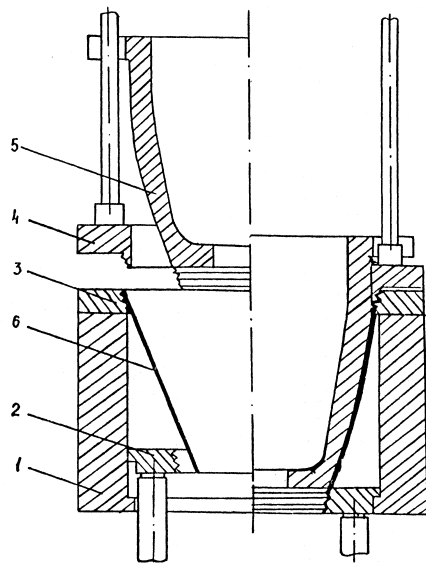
Способ штамповки отбортовки – формовки
